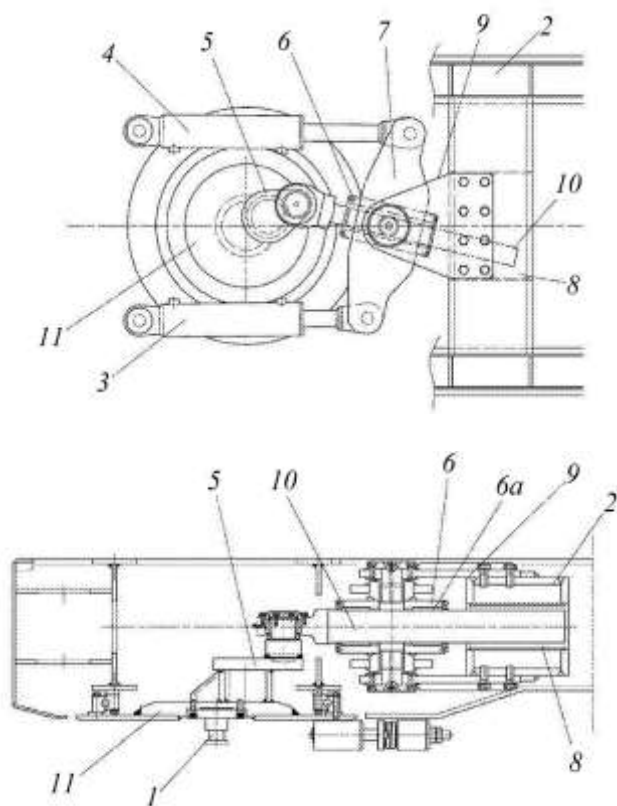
ССУ с рычажным механизмом управления положением колес полуприцепа
